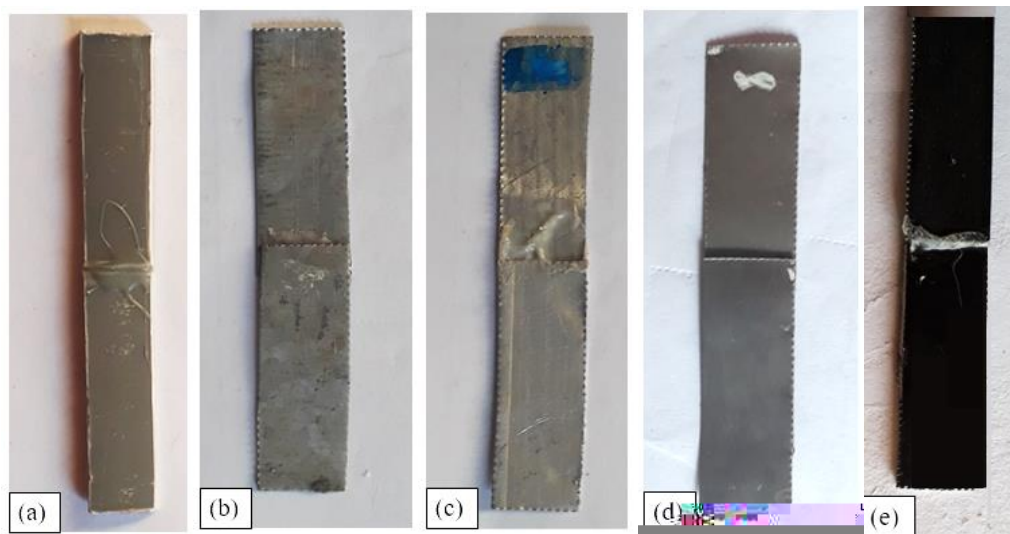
Eprouvettes assemblées par acrylique modifié (a) PVC (b) acier galvanisé (c) aluminium (d) acier inox (e) PE.
